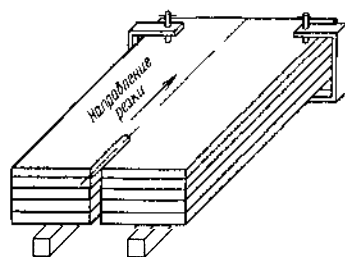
Пакетная резка листов стали с зажатием пакета со стороны, противоположной началу резки
